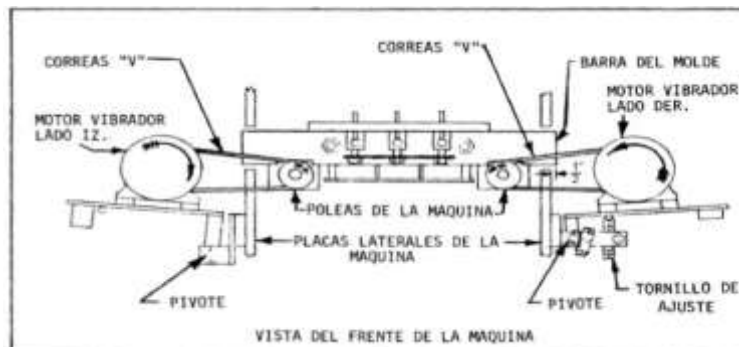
Vista frontal de la máquina (Fuente: Besser Company)
